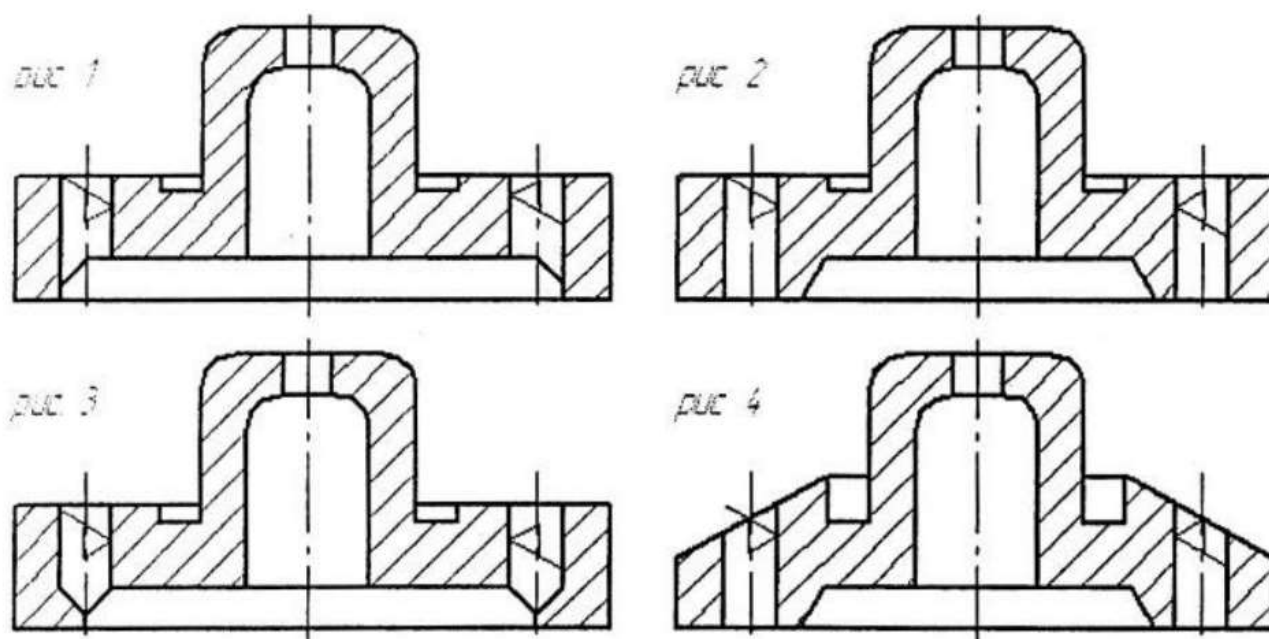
Примеры правильной и неправильной конструкции детали для обработки отверстий
